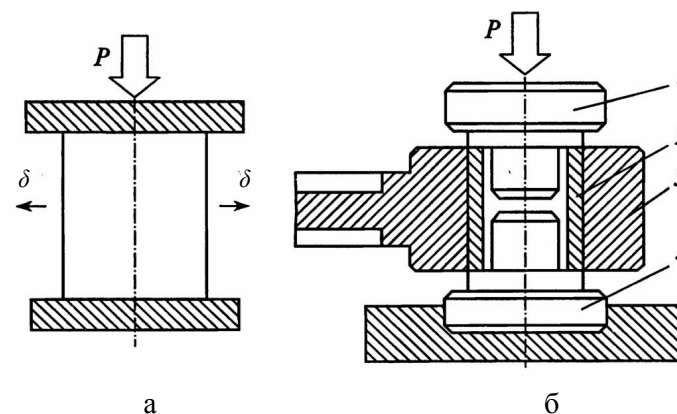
Пластическое деформирование осадкой: а – принципиальная схема; б – осадка давлением втулки верхней головки шатуна; 1, 4 – оправки; 2 – втулка; 3 – шатун
